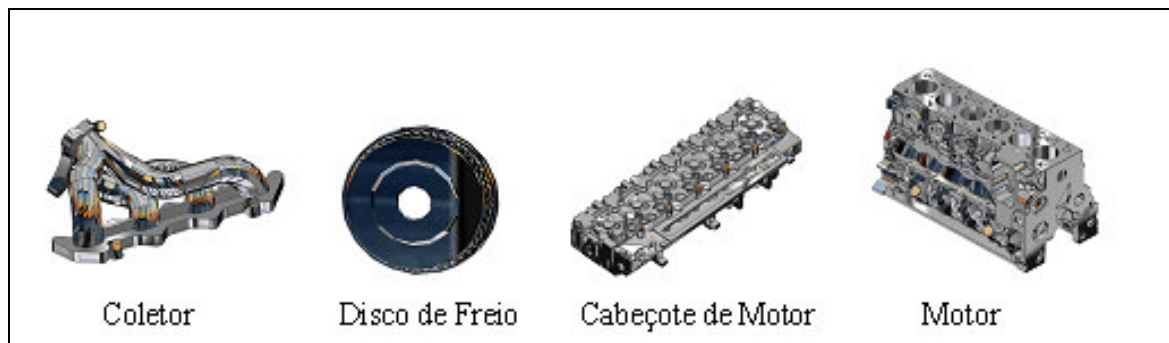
Componentes fabricados na indústria automotiva de ferro fundido cinzento.
